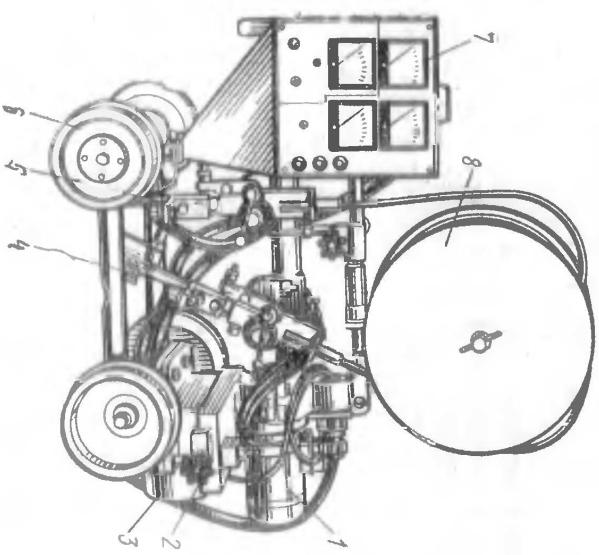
Трактор ТС58 для двухдуговой сварки под флюсом:
